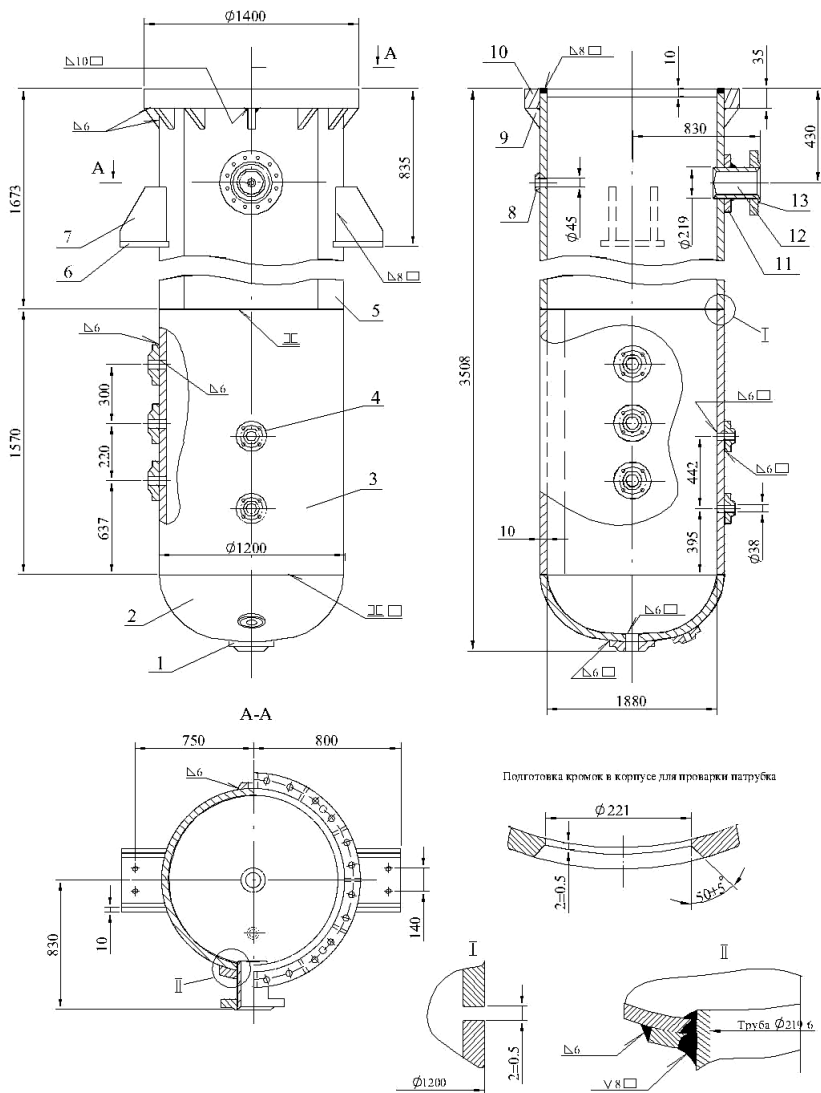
Корпус подогревателя высокого давления: 1 – фланец; 2 – днище; 3 – обечайка нижняя; 4 – фланец; 5 – обечайка верхняя; 6 – плита опорной лапы; 7 – ребро опорной лапы; 8 – наварыш; 9 – ребро; 10 – фланец; 11 – накладка; 12 – патрубок; 13 – фланец
